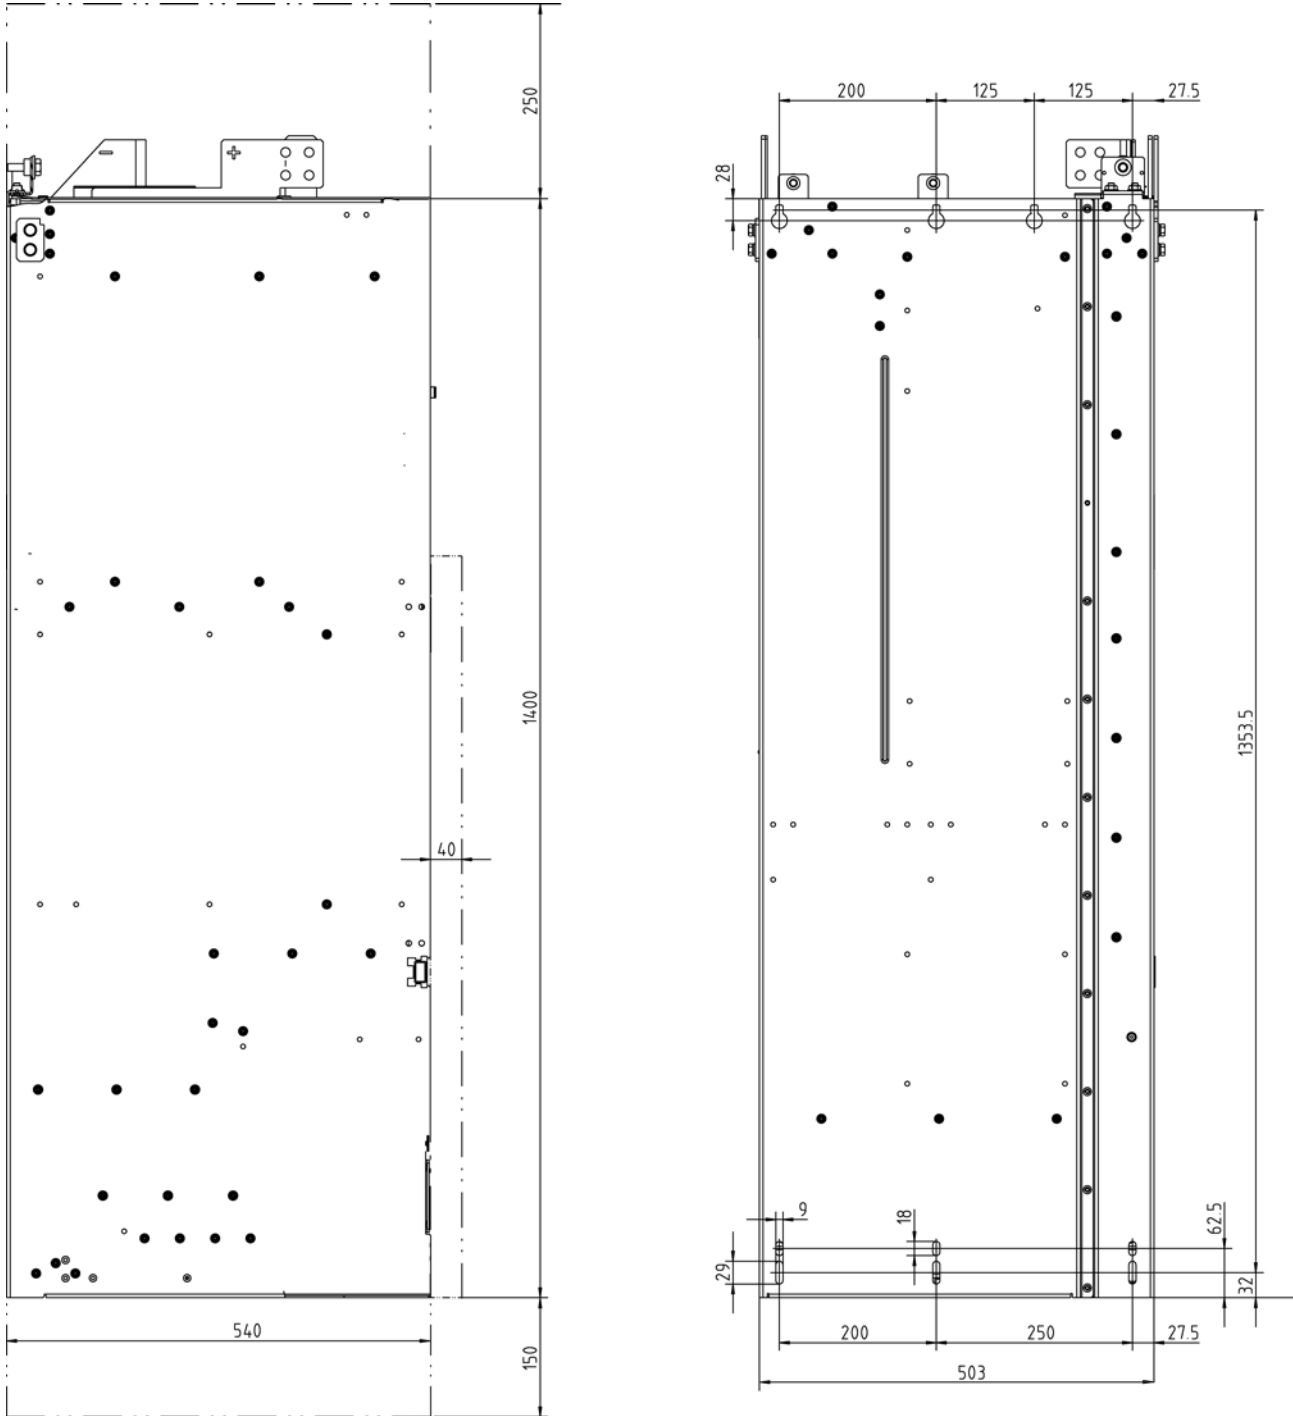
HX 型调节型电源模块的外形尺寸图 侧视图和背视图
